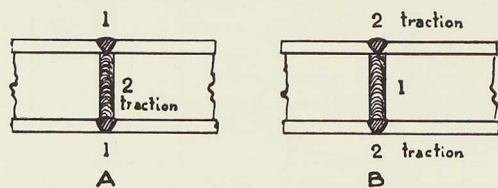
Soudure bout à bout de deux éléments en double T, suivant deux ordres d'exécution différents.
